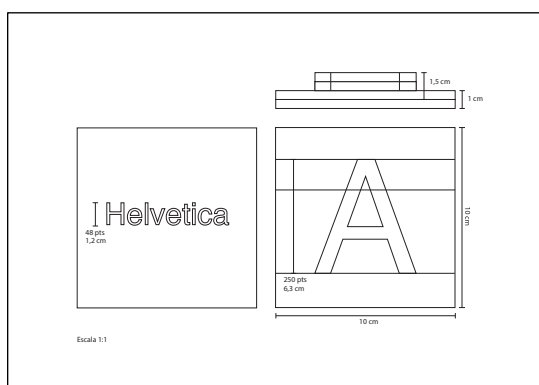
Desenho técnico de placa tátil (fonte: a autora)
